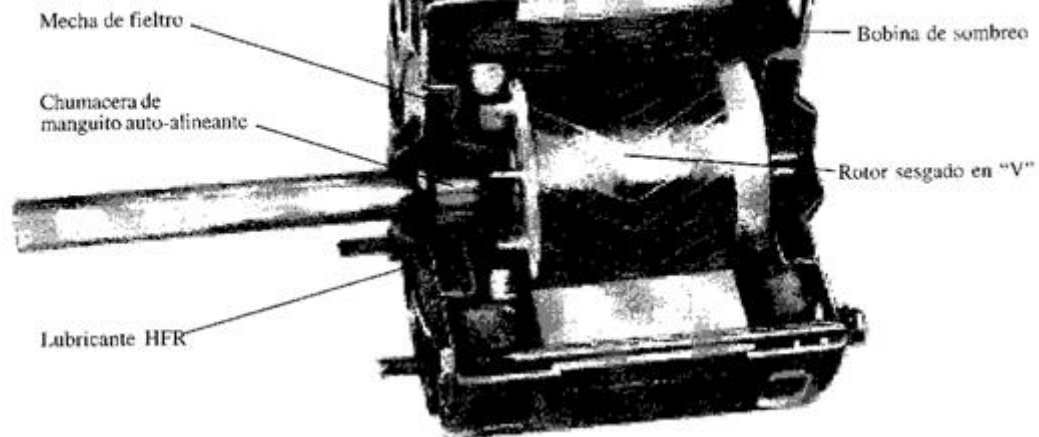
Vista de corte de un motor de polos sombreados.
